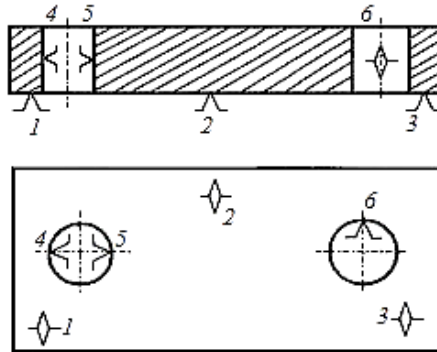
Схема базування заготовки з двома отворами [2]
